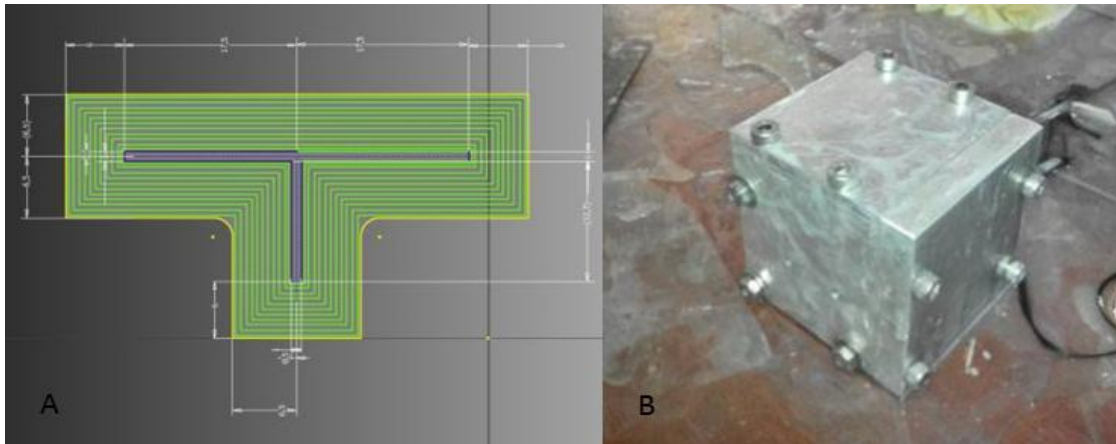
A) DIAGRAMA DE ENROLLADO B) MOLDE CERRADO.
